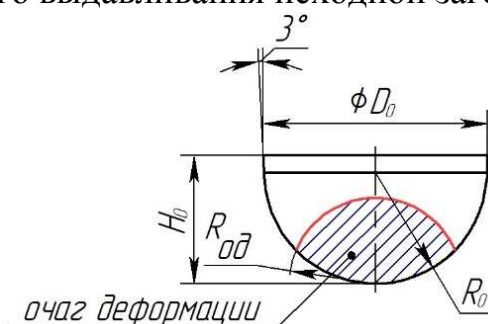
Эскиз осесимметричной штампованной заготовки со сферическим торцем
